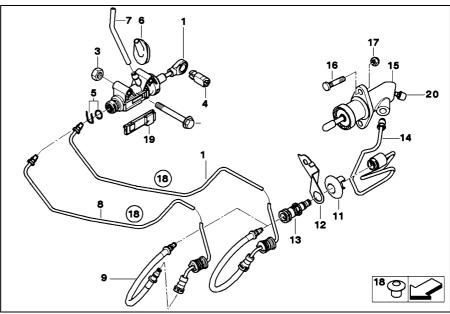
Привод управления сцепления. 1 - главный цилиндр; 2 - палец подвески (болт (М6х45)); 3 - гайка (М6); 4 - штифт; 5 - соединитель с кольцом; 6, 11, 18 - наконечник; 7 - шланг; 8, 10, 14 - трубопровод; 9 - шланг; 12 - держатель; 13 - дроссельный клапан; 15 - рабочий цилиндр; 16 - болт (М8); 17 - гайка (М8); 19 - модуль выключения сцепления; 20 - штуцер прокачки.
